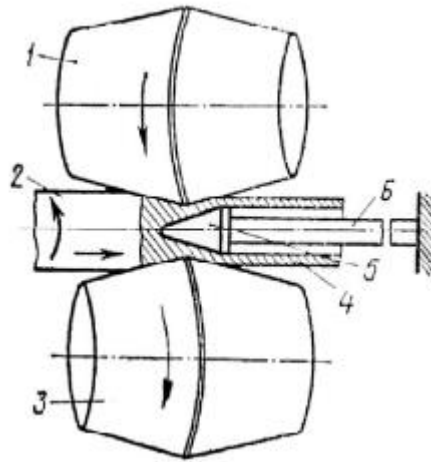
Схема поперечно-гвинтової прокатки
